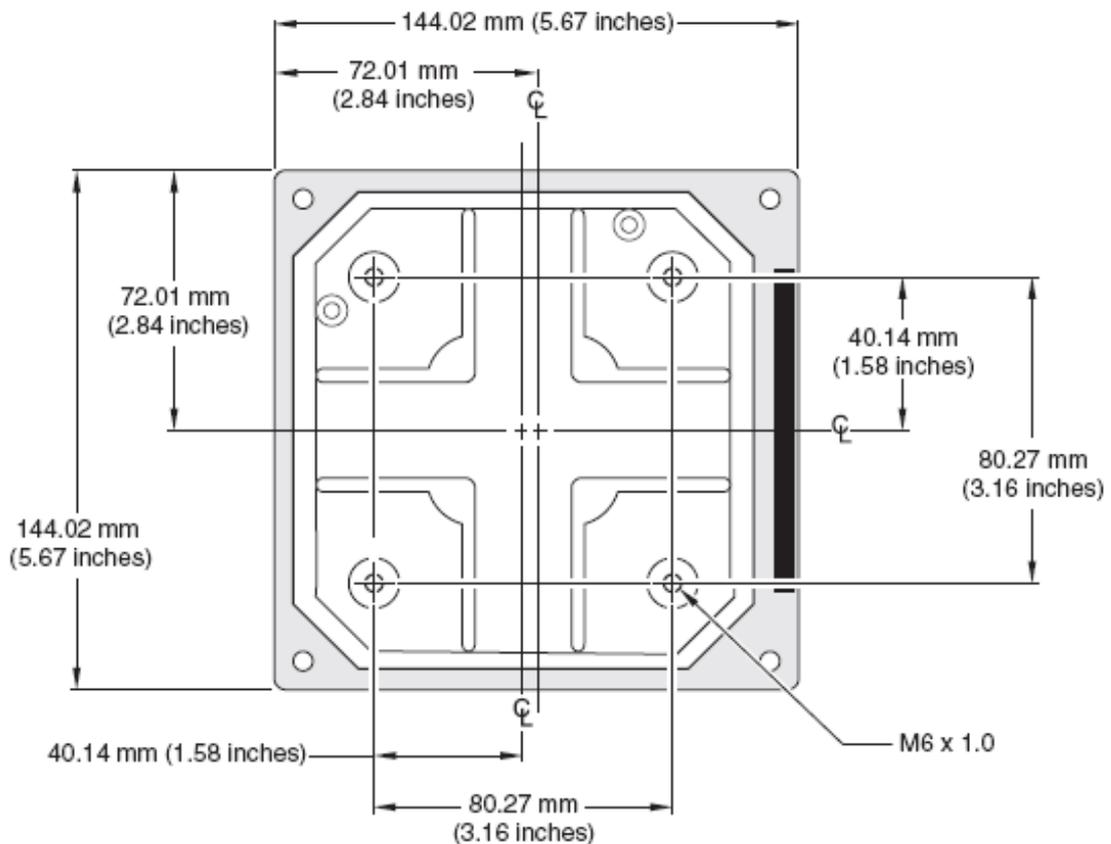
Dimensiones del hueco del panel para montaje del controlador
